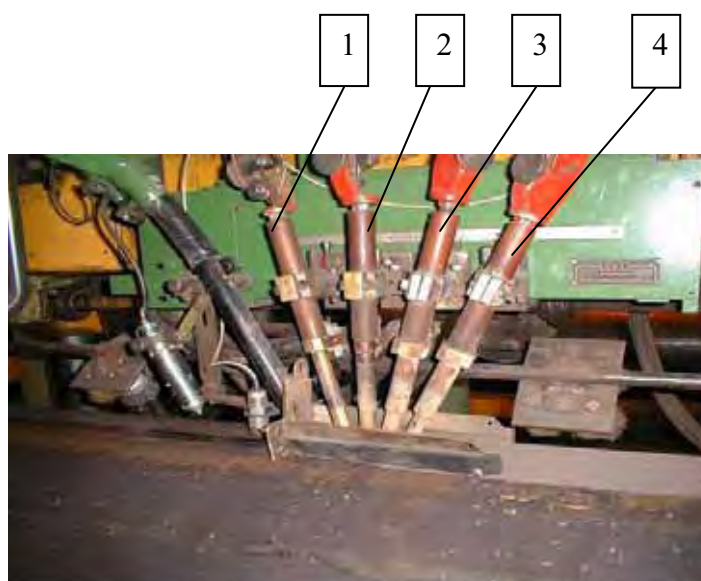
Processo de soldagem por arco submerso com 4 eletrodos
